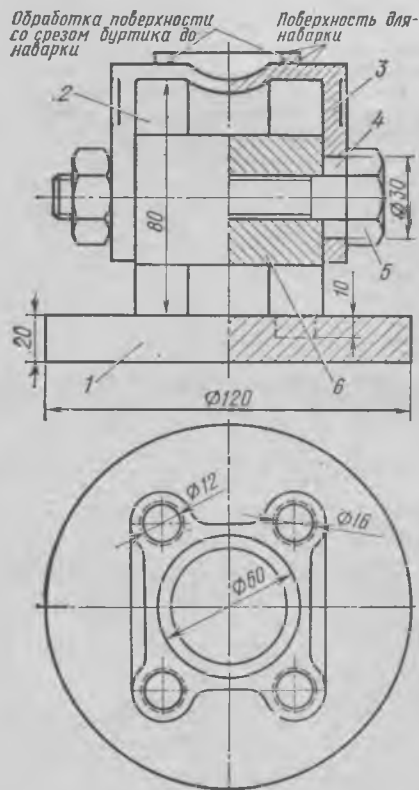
Приспособление для наварки торцевых поверхностей фланцев карданного вала охлаждения генератора:
